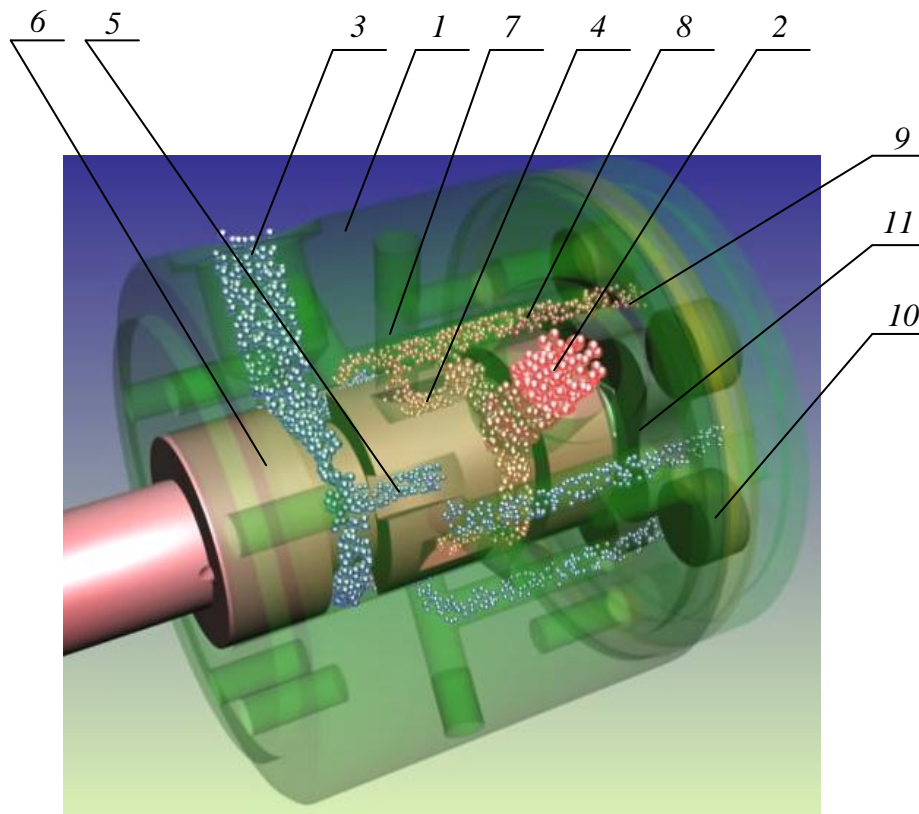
Принцип работы цапфенного распределения рабочей жидкости: 1 – корпус; 2 – входное отверстие; 3 – выходное отверстие; 4 – пазы нагнетания; 5 – пазы слива; 6 – вал; 7 – радиальные отверстия; 8 – торцевые отверстия; 9 – рабочие камеры; 10 – охватывающий вытеснитель; 11 – охватываемый вытеснитель
